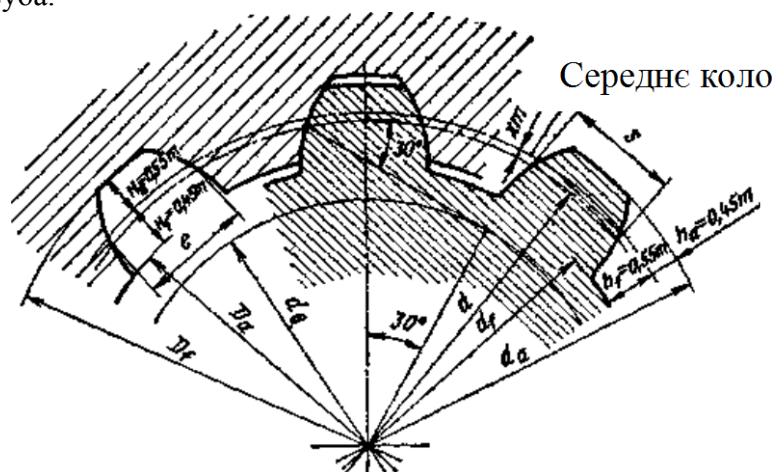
Схема евольвентного шліцьового з'єднання
